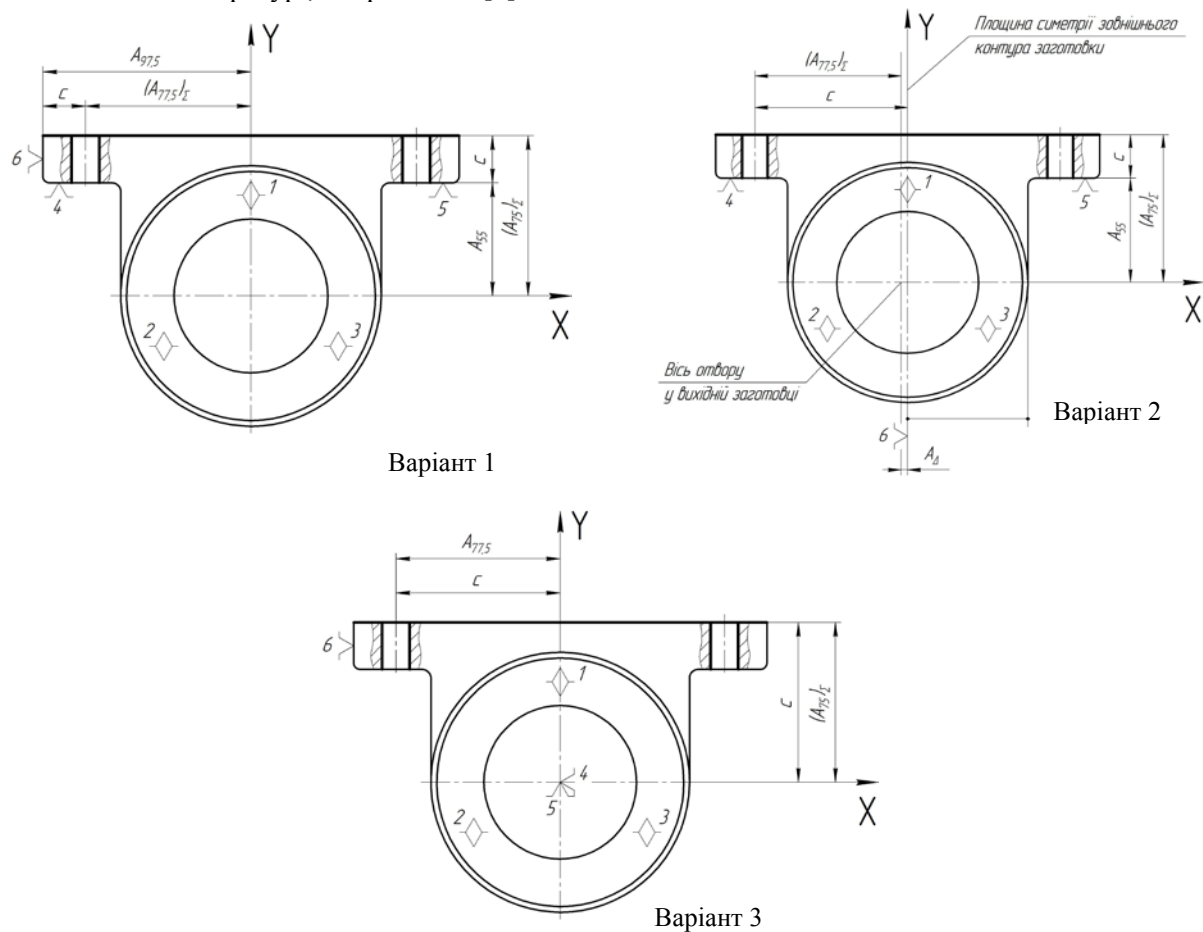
Варіанти схеми базування заготовки деталі типу «Корпус підшипника» на першій операції механічної обробки з технологічними розмірними ланцюгами для визначення похибки базування
